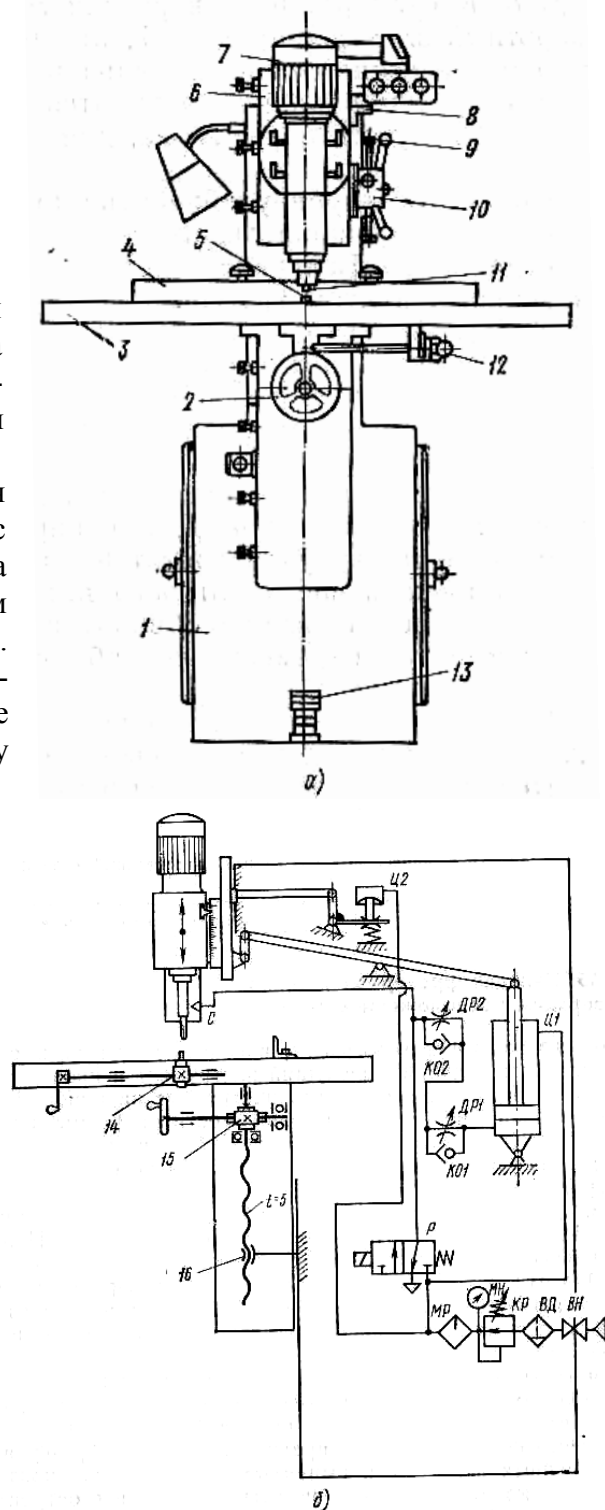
Фрезерный станок с верхним расположением шпинделя ВФК-2:
